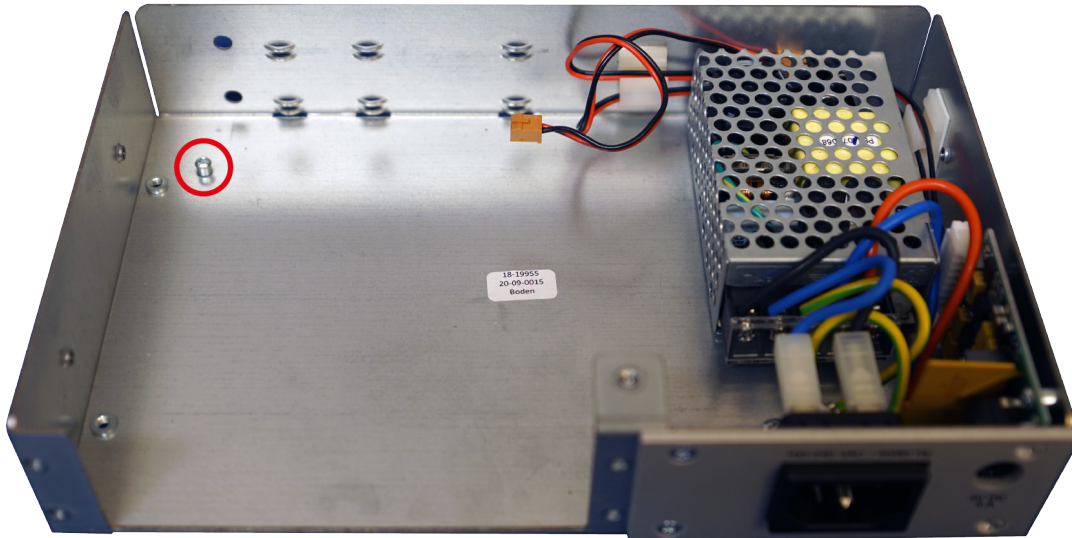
Erdungsschraube im Auslieferungszustand des Chassis
